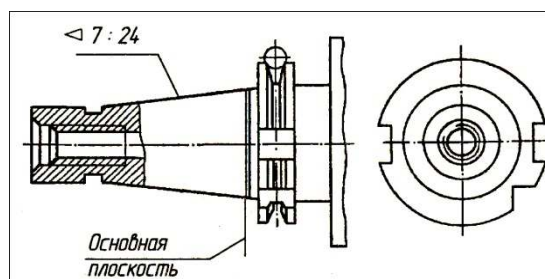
Хвостовик шпиндельных оправок станков сверлильно-фрезерно-расточной группы
